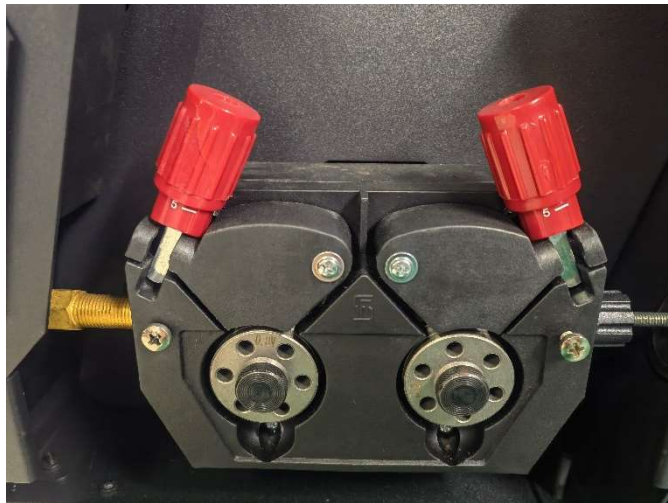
Montage der Messingdüse für die Drahtzuführung
